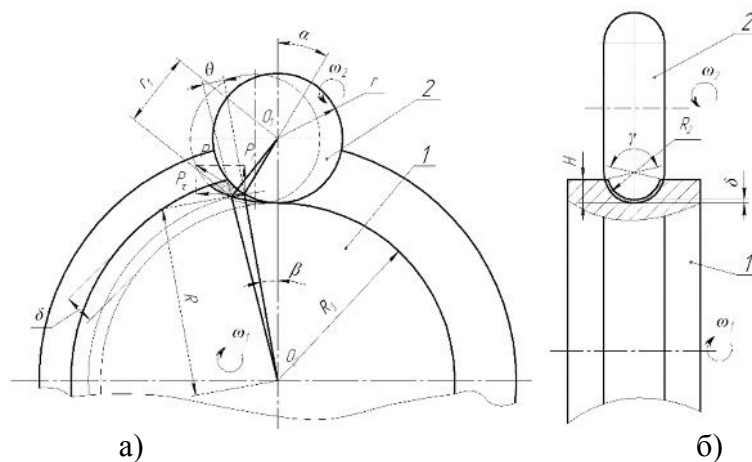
Розрахункова схема для дослідження зміцнення поверхневого шару гвинтової канавки поверхневим пластичним деформуванням фасонним циліндричним роликом 2 а) поздовжній переріз; б) поперечний переріз; 1 - заготовка
